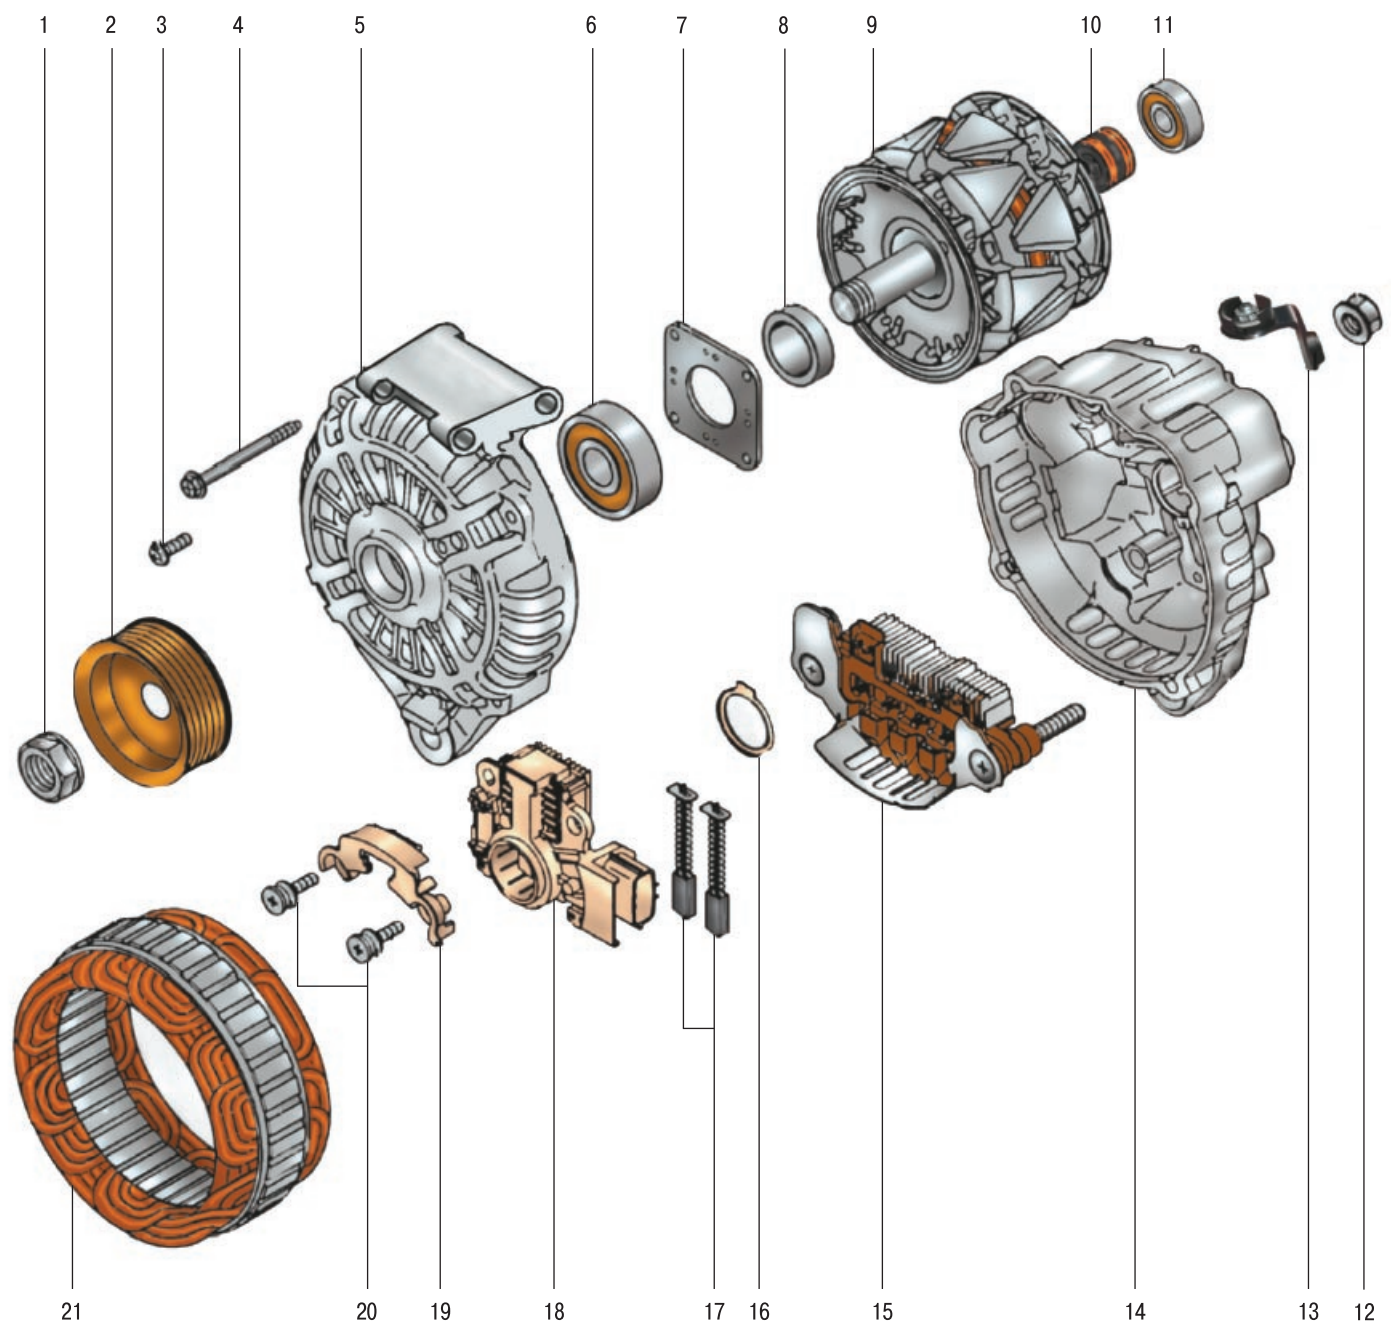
Детали генератора: 1 – гайка крепления шкива; 2 – шкив; 3 – винт крепления прижимной пластины переднего подшипника; 4 – стяжной болт крышек генератора; 5 – крышка со стороны привода; 6 – передний подшипник ротора; 7 – прижимная пластина подшипника; 8 – дистанционное кольцо; 9 – ротор; 10 – контактные кольца; 11 – задний подшипник ротора; 12 – гайка контактного болта; 13 – клемма контактного болта; 14 – крышка со стороны контактных колец; 15 – выпрямительный блок; 16 – уплотнительная прокладка; 17 – щетки; 18 – щеткодержатель с регулятором напряжения; 19 – накладка; 20 – винты крепления щеткодержателя; 21 – статор
